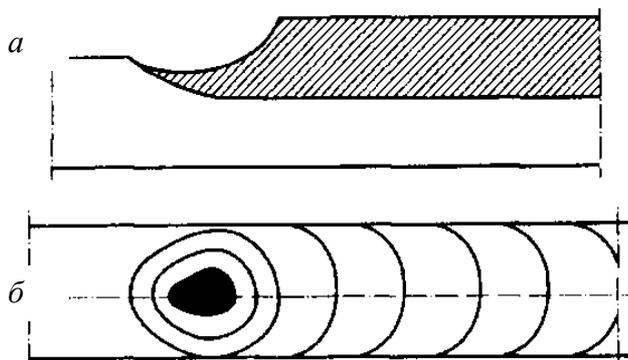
Кратер сварного шва: *a* – сечение по кратеру; *б* – вид сверху
